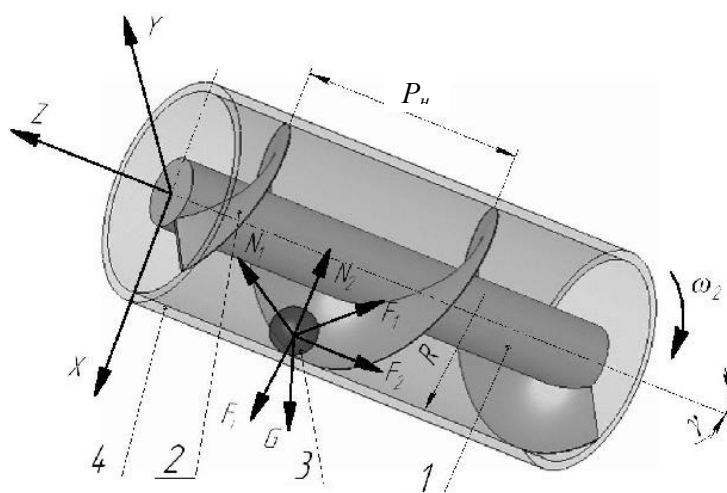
Розрахункова схема для визначення мінімальної частоти обертання циліндричного кожуха гвинтового конвеєра: 1 - вал; 2 – гвинтовий робочий орган; 3 – частинка матеріалу; 4 – обертовий циліндричний кожух
